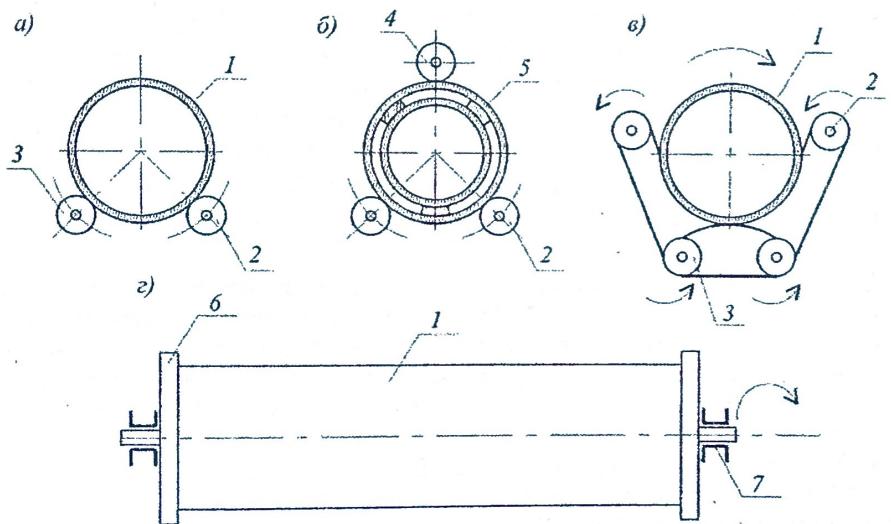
Типы центрифуг(СНиП II-21-75) а) - роликовая, б) - барабанная, в) - гиростатическая, г) - осевая; 1 - форма, 2 - опорный ролик, 3 - ролик, 4 - привод, 5 - барабан, 6 - планшайба, 7 - опорный подшипник, приводной
